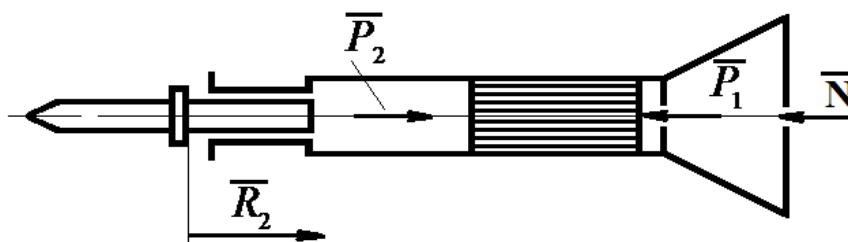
Схема сил, действующих на корпус пневмомолотка
